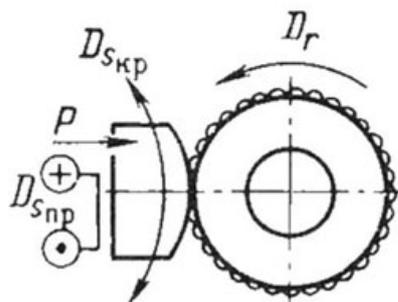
Схема притирки цилиндрического сопряжения
